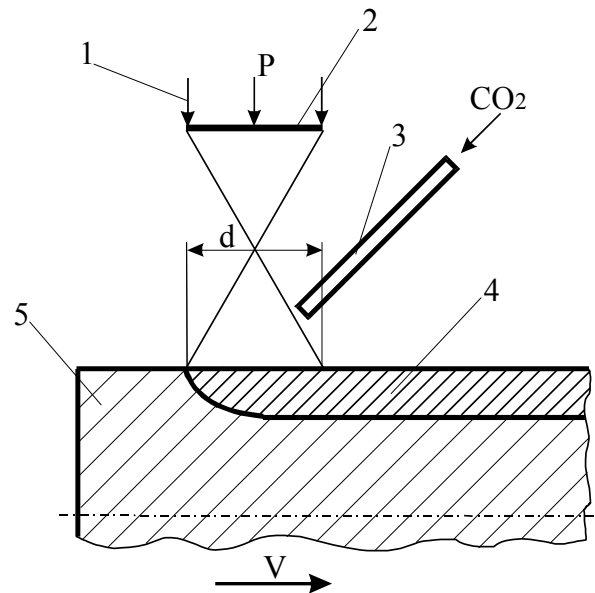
Принципова схема лазерного опромінювання контактної поверхні проводу: 1 – пучок лазерного променя; 2 – фокусуюча лінза; 3 – патрубок з вуглецевим газом; 4 – сформований шар; 5 – зразок контактної поверхні проводу
